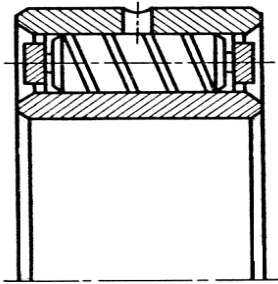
Радиальный роликовый подшипник с витыми роликами
